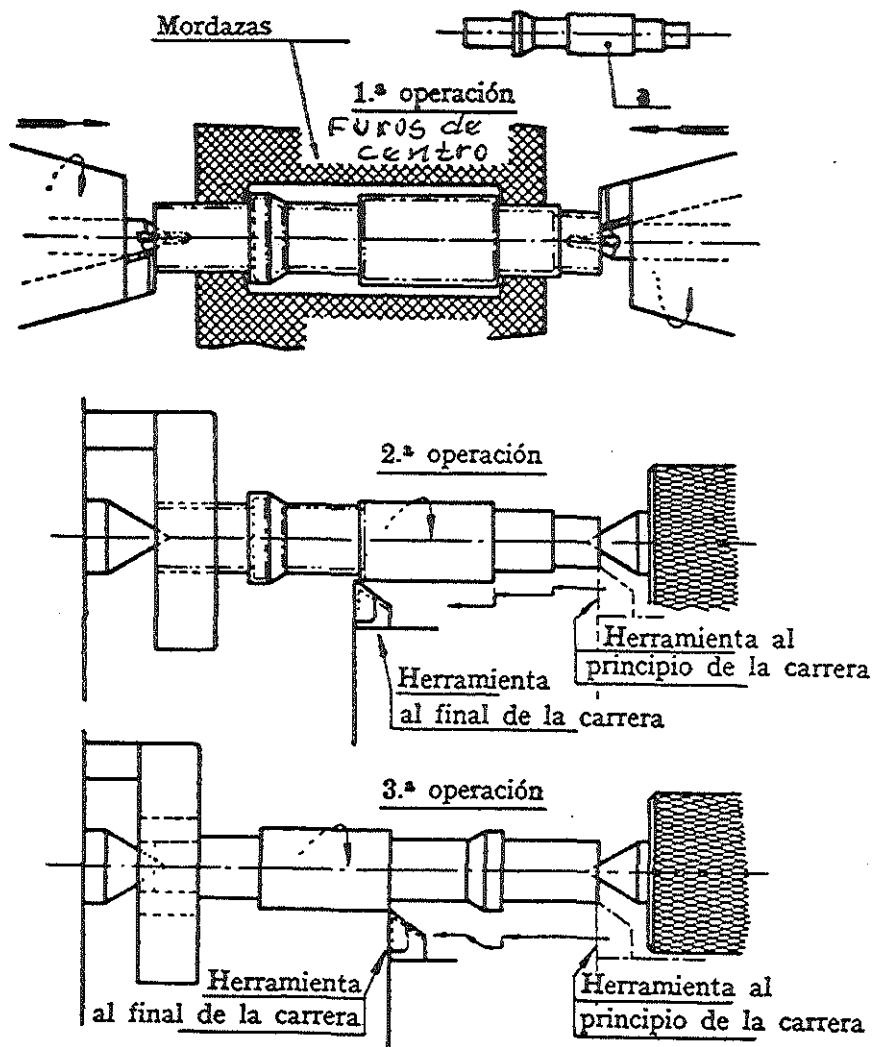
Processo de usinagem para obter o pino desenhado em a.
